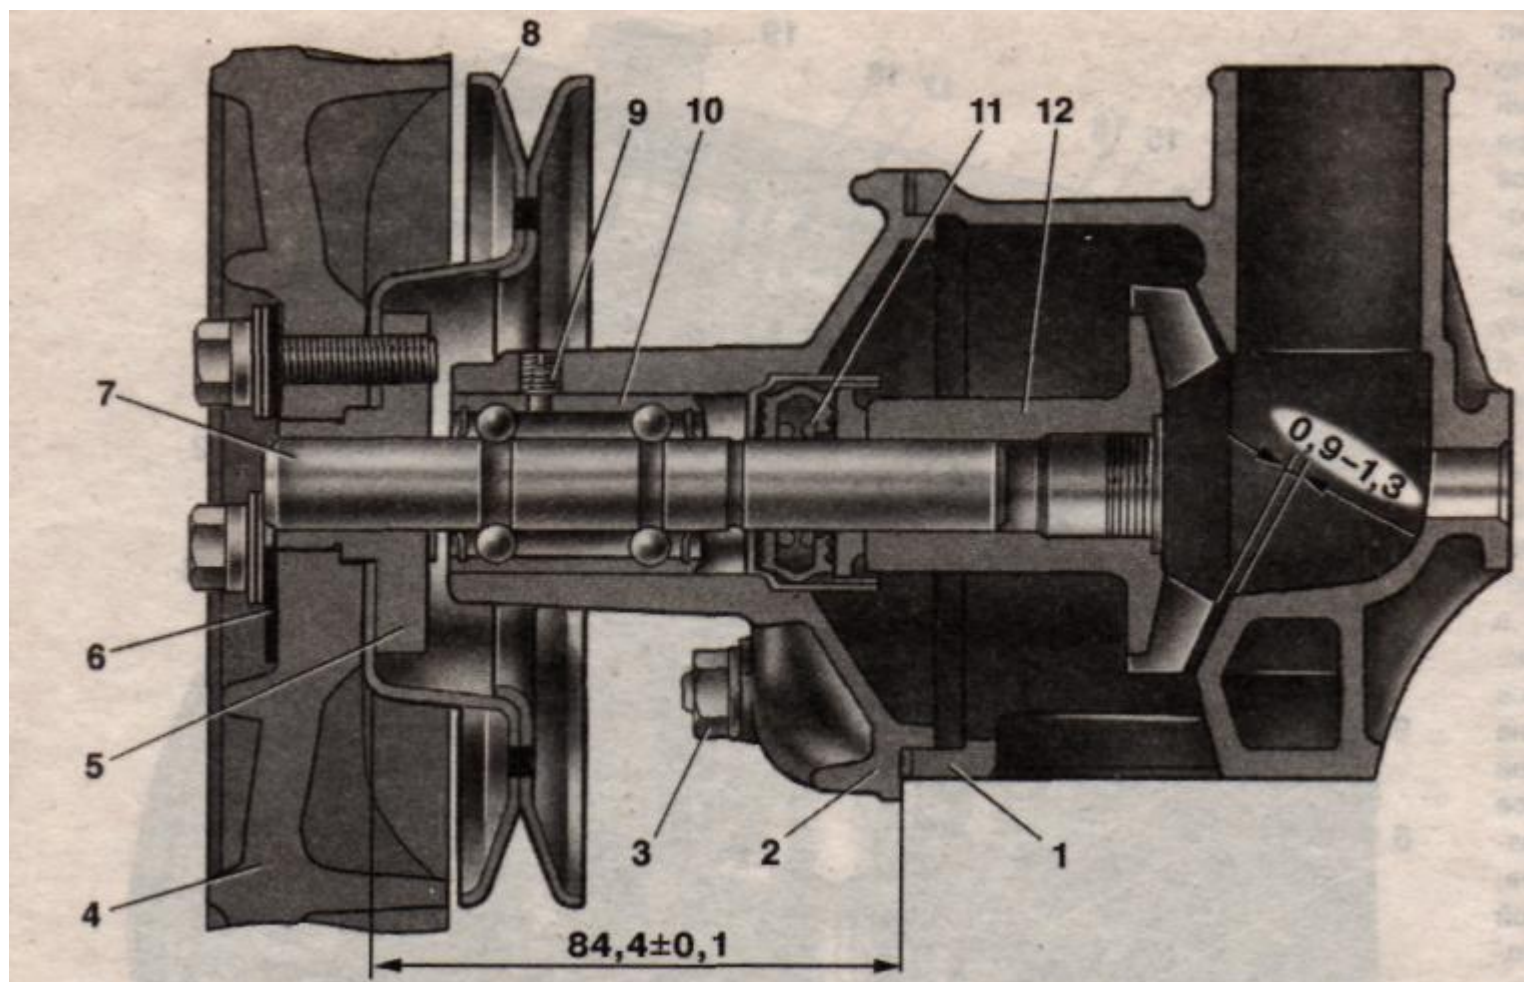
Поздовжній розріз насоса охолодної рідини: 1 - корпус; 2 - кришка; 3 - гайка кріплення кришки насоса; 4 - вентилятор; 5 - маточина шківів; 6 - накладка; 7 - валик; 8 - шків; 9 - стопорний гвинт підшипника; 10 - підшипник; 11 - сальник; 12 - крильчатка
